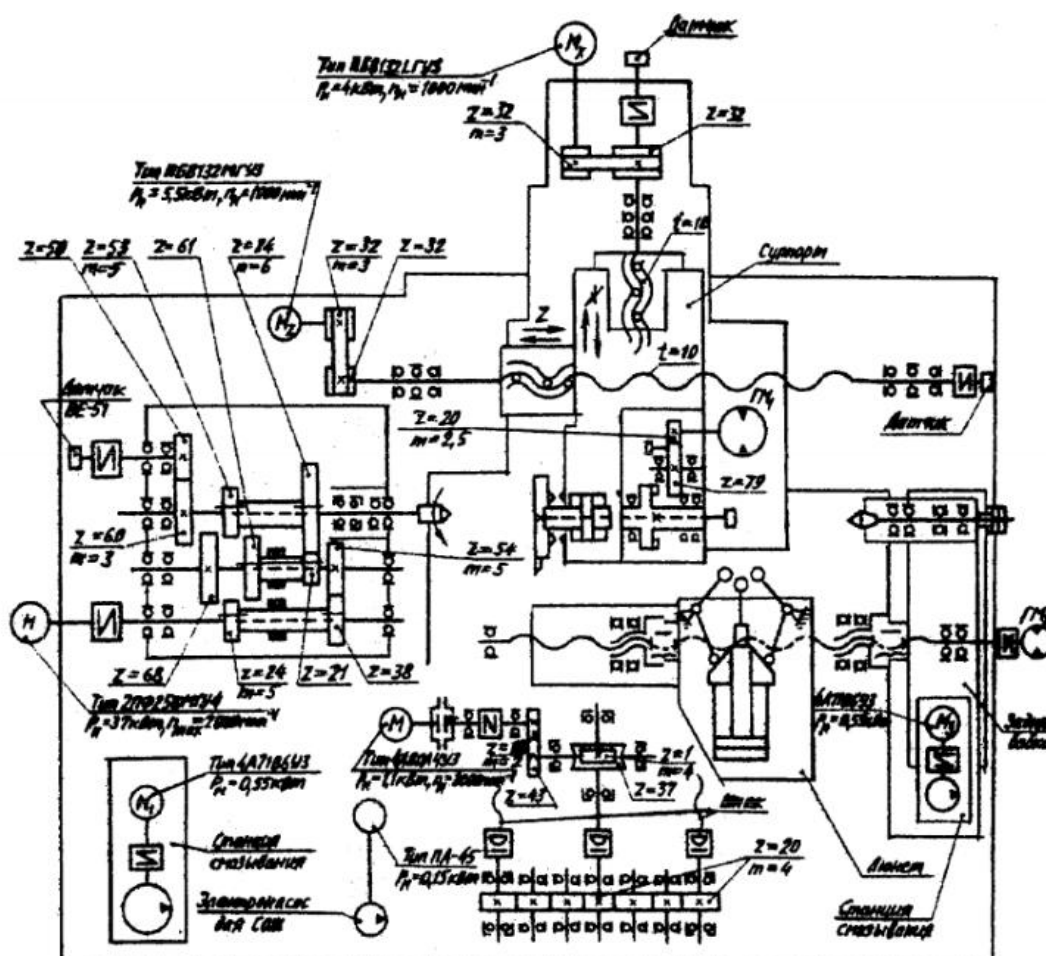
Пример кинематической схемы базового станка 1740P3
